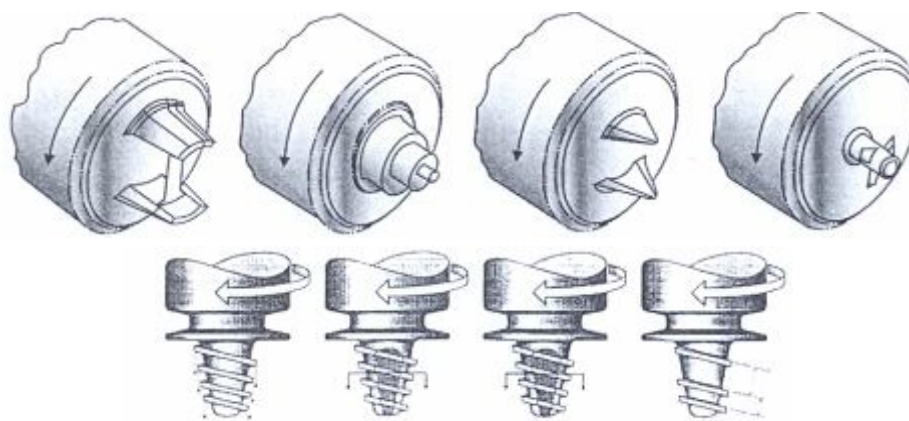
Возможные конструктивные решения инструментов для сварки трением с перемешиванием, приведенные в литературных источниках [3–5].
